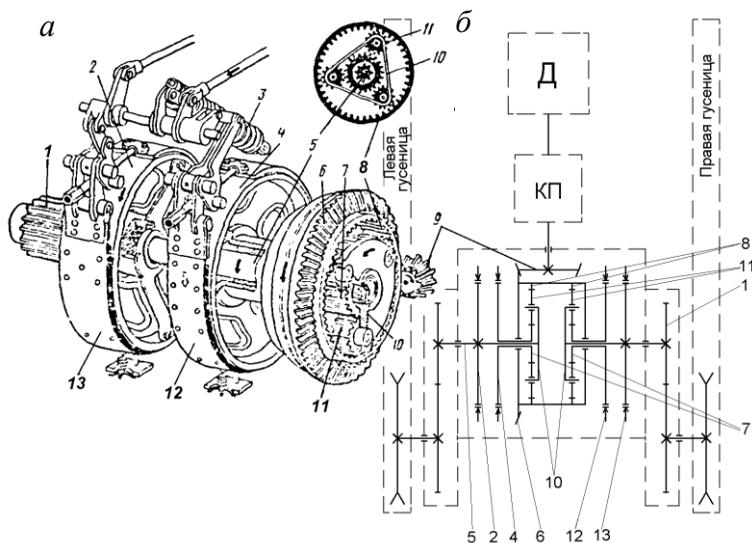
Поворот гусеничного трактора с помощью планетарного механизма:
